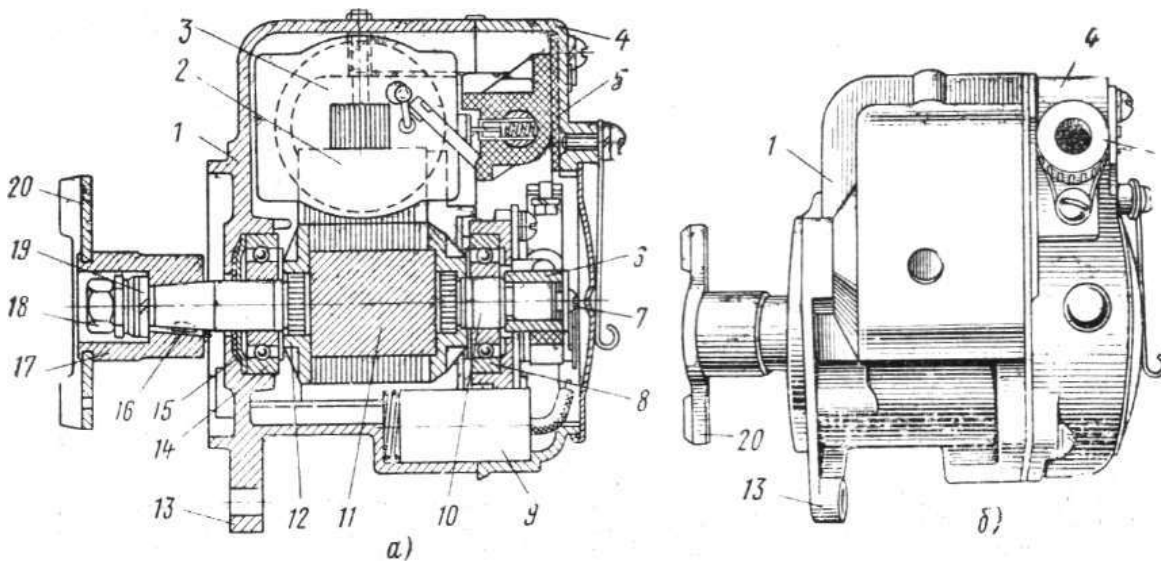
Магнето М24-А1: а — продольный разрез, б — общий вид; 1 — корпус. 2 — магнитопровод. 3 — автотрансформатор, 4 — крышка, 5 — вывод тока высокого напряжения, 6 — кулачок прерывателя, 7 — винт, 8, 14 — шарикоподшипники, 9 — конденсатор. 10 — валик ротора. 11 — магнит ротора, 12 — корпус ротора, 13 — фланец, 15 — уплотнение подшипника, 16 — шпонка. 17 — втулка, 18 — гайка, 19 — стопорное кольцо. 20 — поводок, 18 — приводная муфта. На обе части валика напрессованы внутренние обоймы шарикоподшипника.
